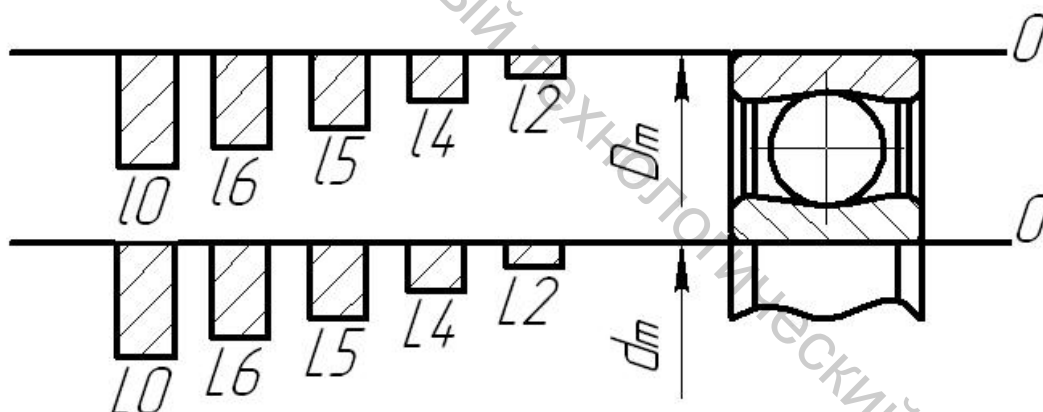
Схемы расположения интервалов допусков колец подшипников качения
